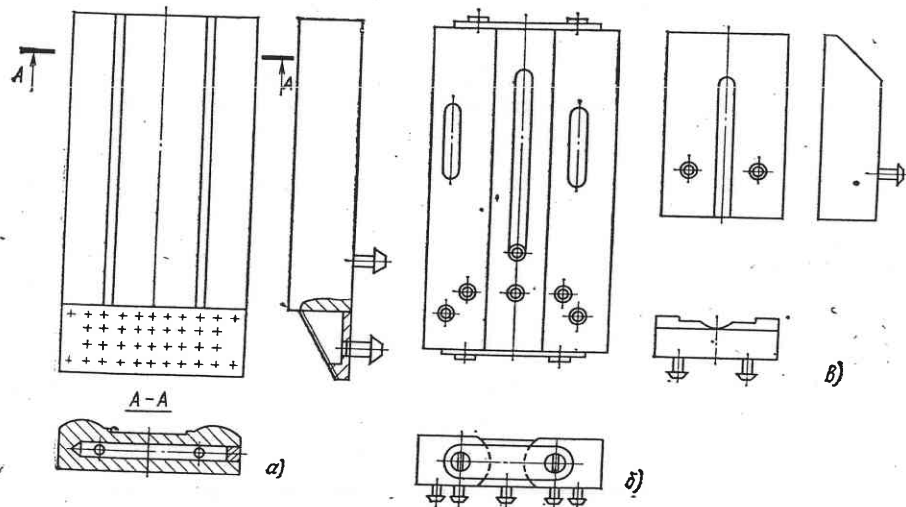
Ползуны для автоматической сварки вертикальных стыков с принудительным формированием шва: а — монолитный со спреером для ЭПС; б — шарнирный для ЭПС; в — монолитный для дуговой сварки порошковой проволокой
